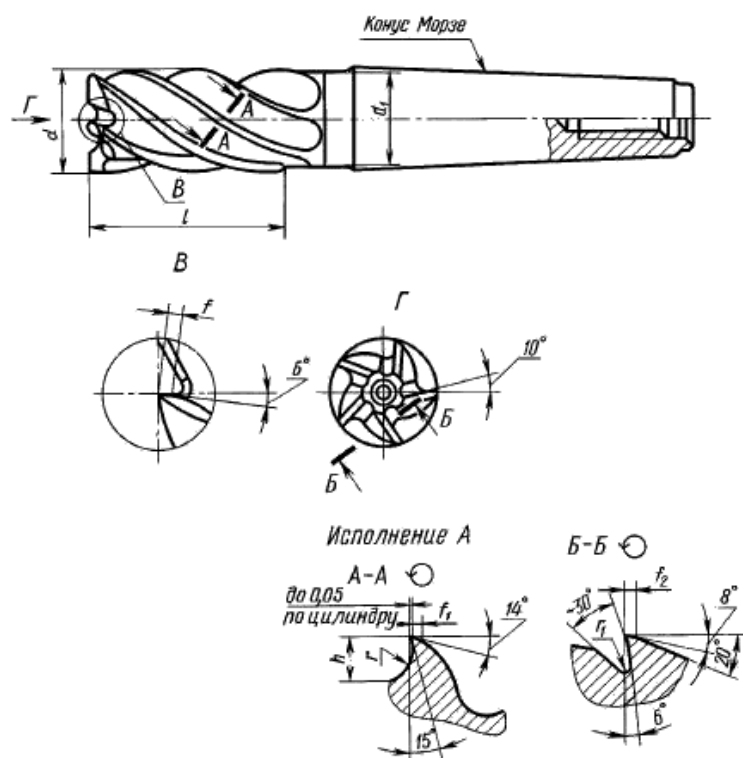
Элементы конструкции и геометрические параметры концевых фрез из быстрорежущей стали
